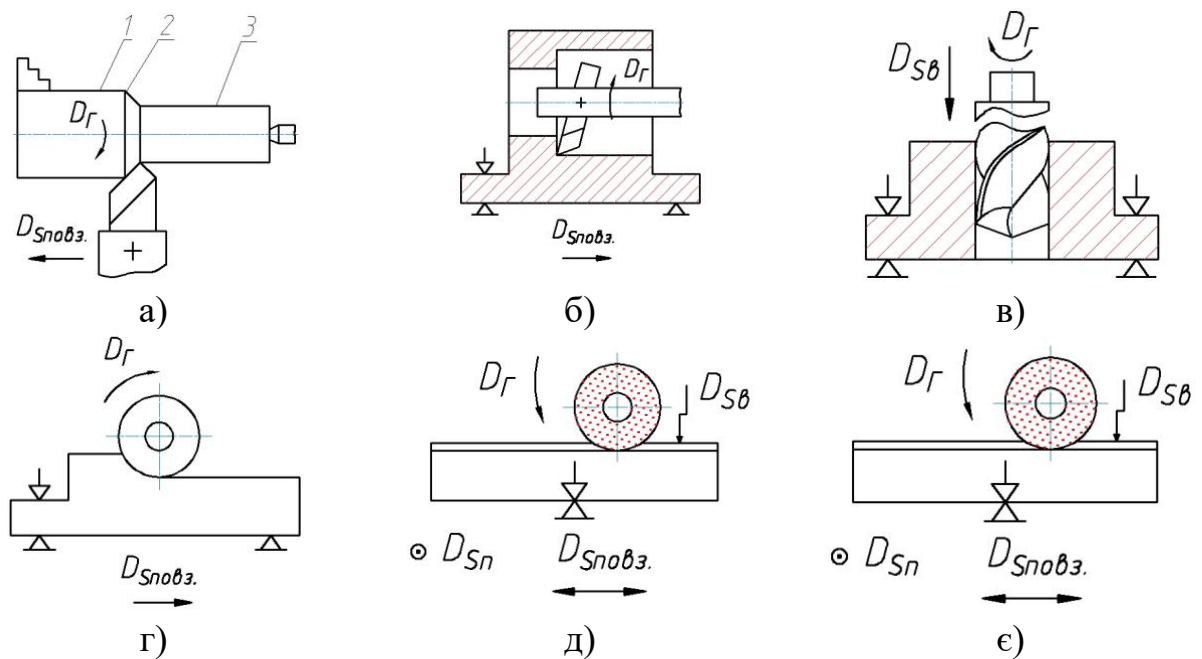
Схеми обробки заготовок: а) – точіння; б) – розточування; в) – свердління; г) – фрезерування; д) – шліфування на круглошліфувальному верстаті; е) – шліфування на плоскошліфувальному верстаті.
